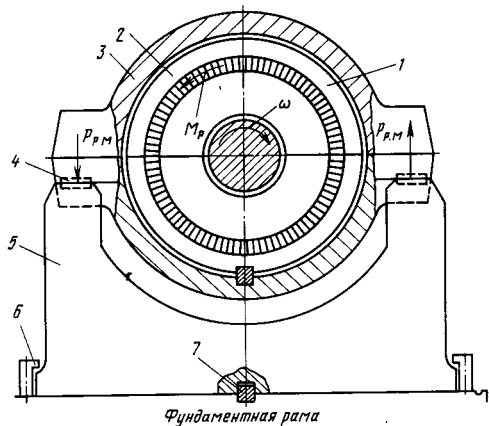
Появление усилия на корпусе подшипника от действия реактивного момента: 1 — вал ротора; 2 — диафрагма; 3 — корпус турбины; 4 — поперечные шпонки лап; 5 — корпус подшипника; 6 — прижимная скоба; 7 — продольная шпонка
